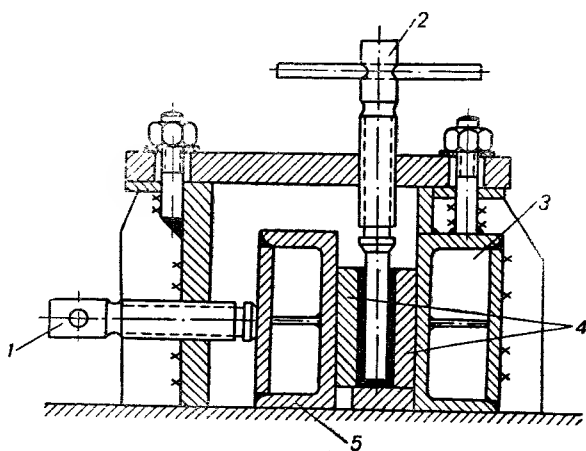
Паровая пресс-форма для опрессовки роторных гильз:
